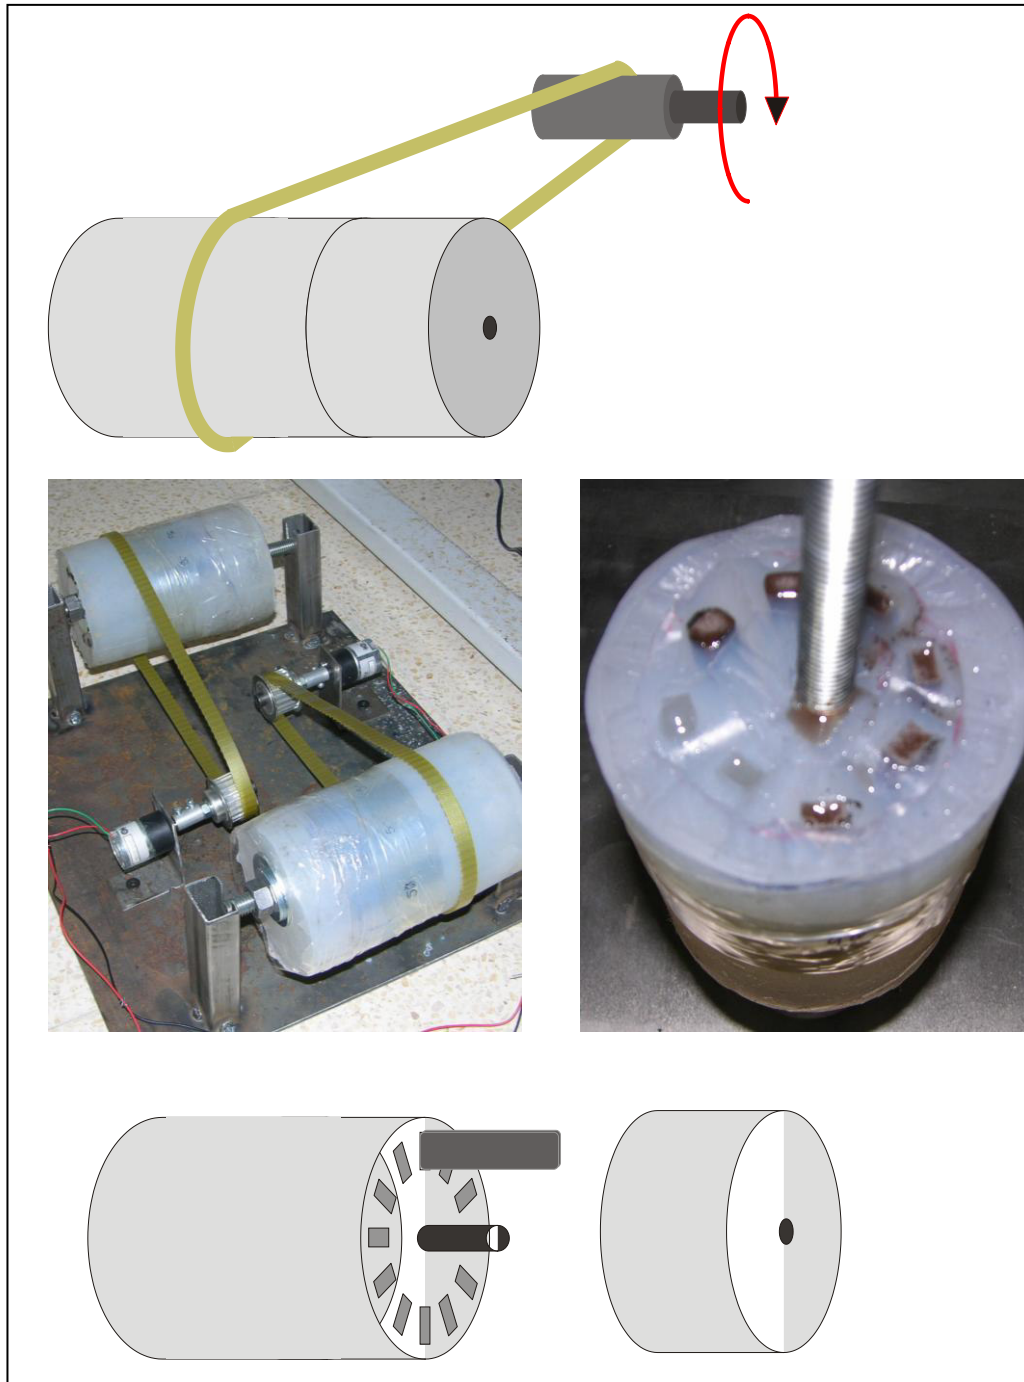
Produção de provetes para ensaios mecânicos: a) Molde em silicone; b) Sistema eletromecânico de acionamento do molde em silicone.
